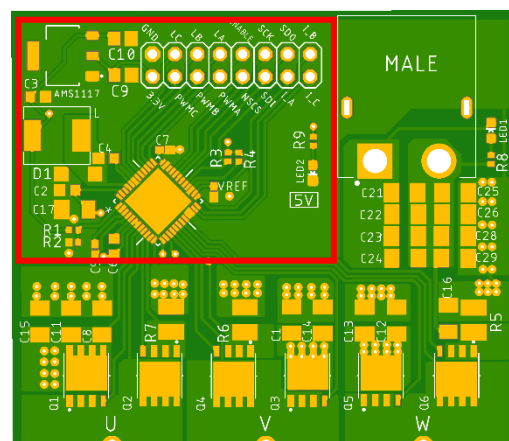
Capa superior de la PCB (Font: Ernest Porqueras)
